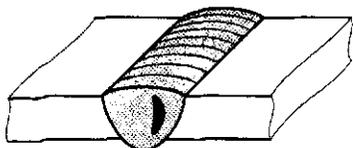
Усадочная раковина в металле сварного шва
